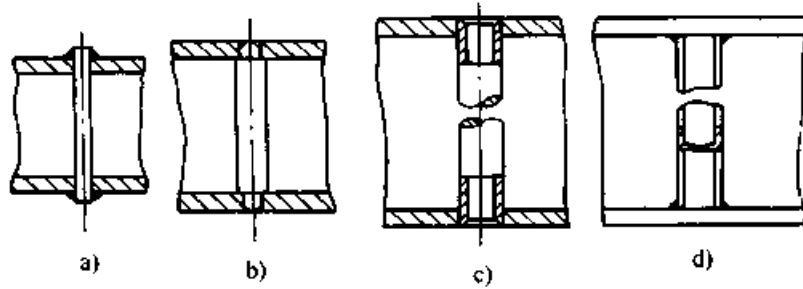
焊接开式机架中两壁板间的连接结构
